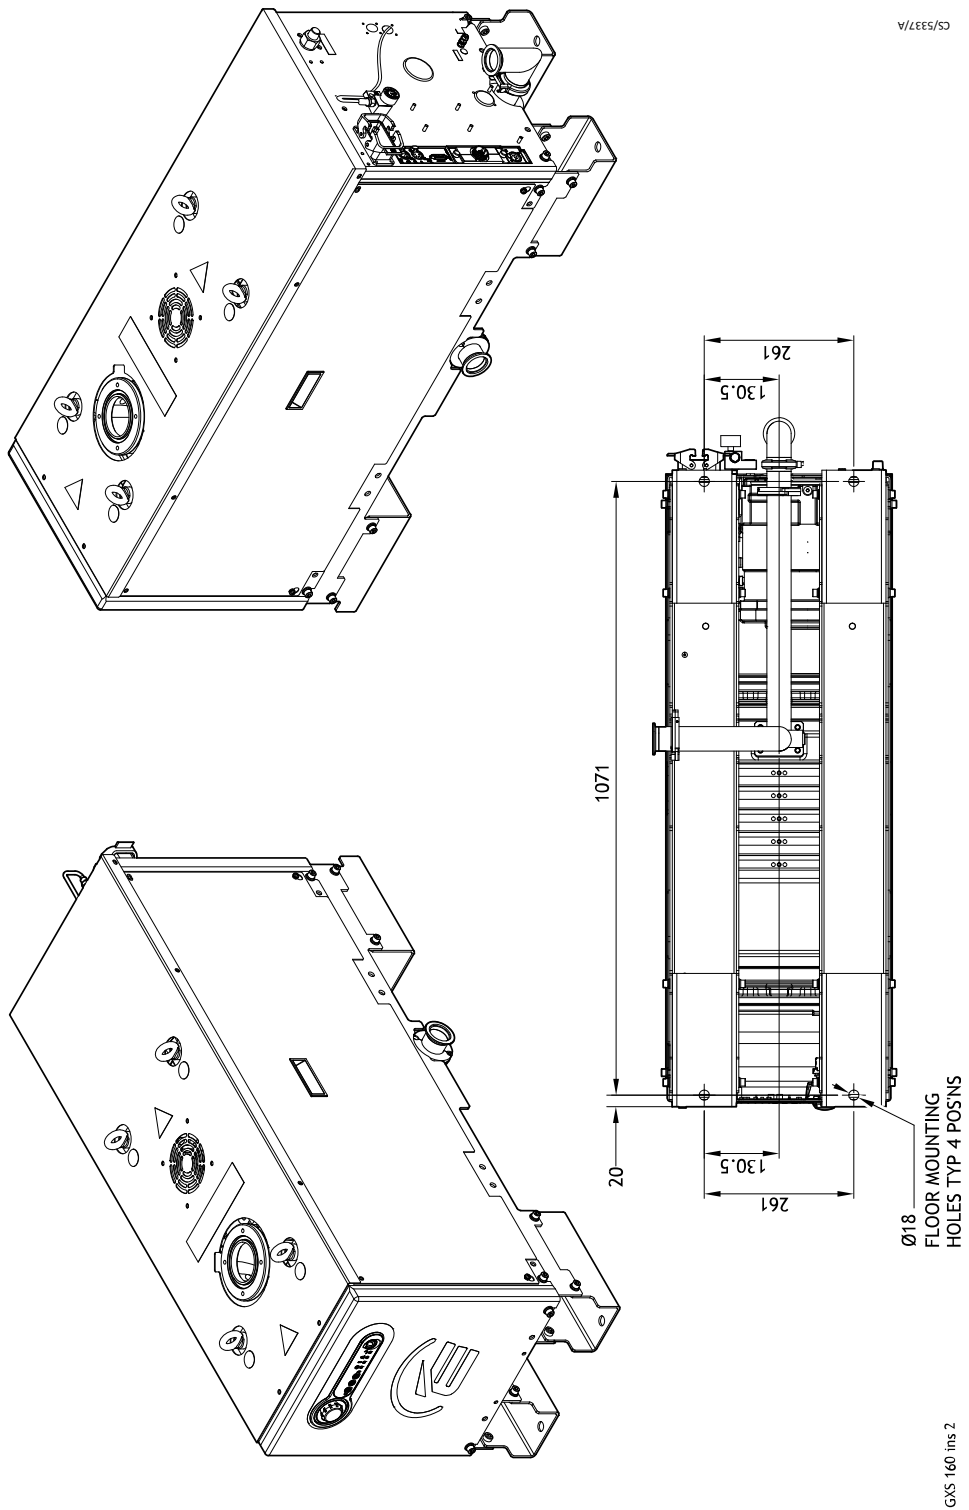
GXS160 Installationszeichnung (Blatt 3)
